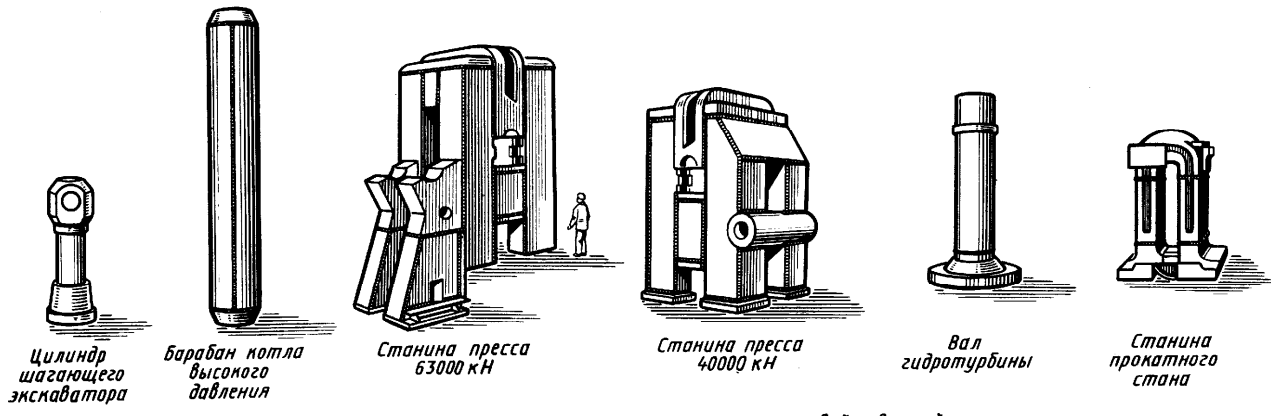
Примеры конструкций, сваренных электрошлаковой сваркой
